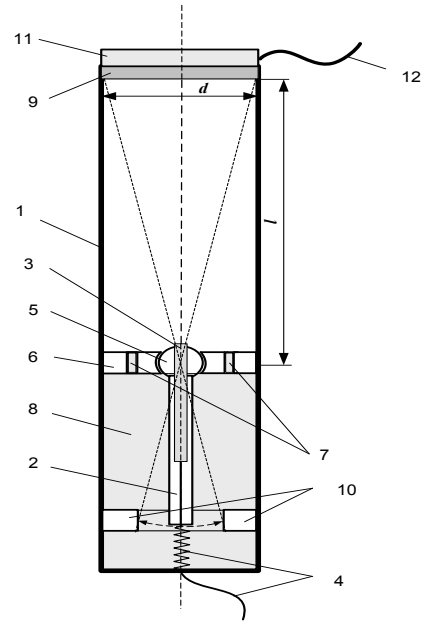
Будова пристрою контролю вертикальності щогли: 1 – трубчастий корпус; 2 – маятник; 3 – лазер; 4 – дріт живлення; 5 – рухома частина шарнірного кріплення; 6 – кільце гасіння коливань; 7 – отвори гасіння коливань; 8 – амортизаційна рідина; 9 – світлочутливе поле; 10 – кільце обмеження ходу маятника; 11 – кодер; 12 – з’єднувальний кабель
